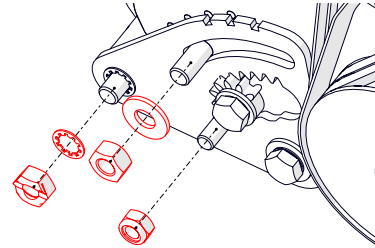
A – Die drei Befestigungselemente wie abgebildet entfernen.
